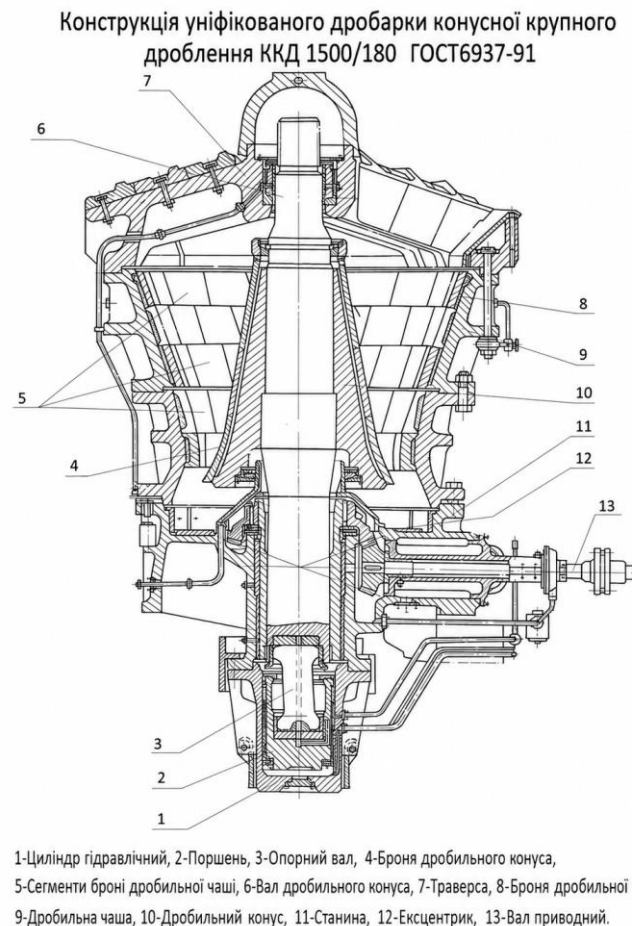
Креслення дробарки ККД 1500×180
